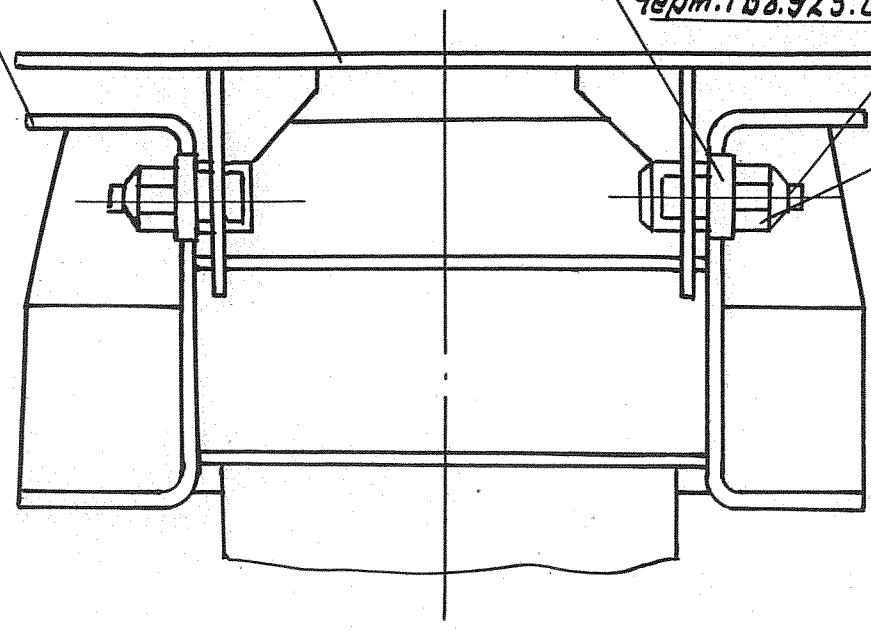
Крепление крышки с активной частью трансформатора.
